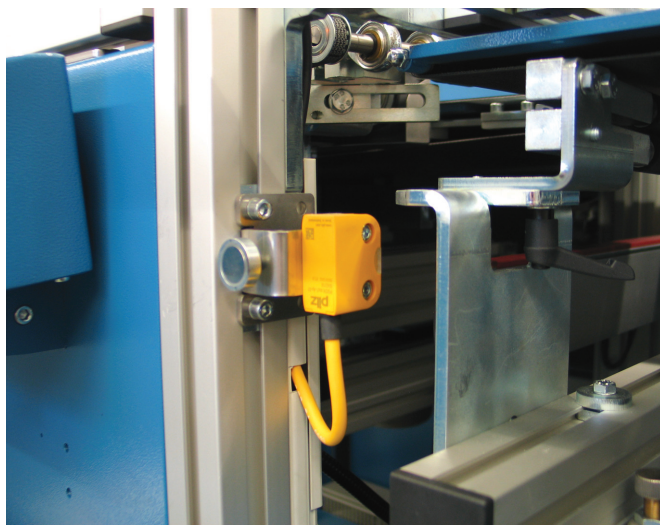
Die magnetischen Sicherheitsschalter „PSENmag“ lassen sich dank ihrer kompakten Bauform gut in Maschinen integrieren
